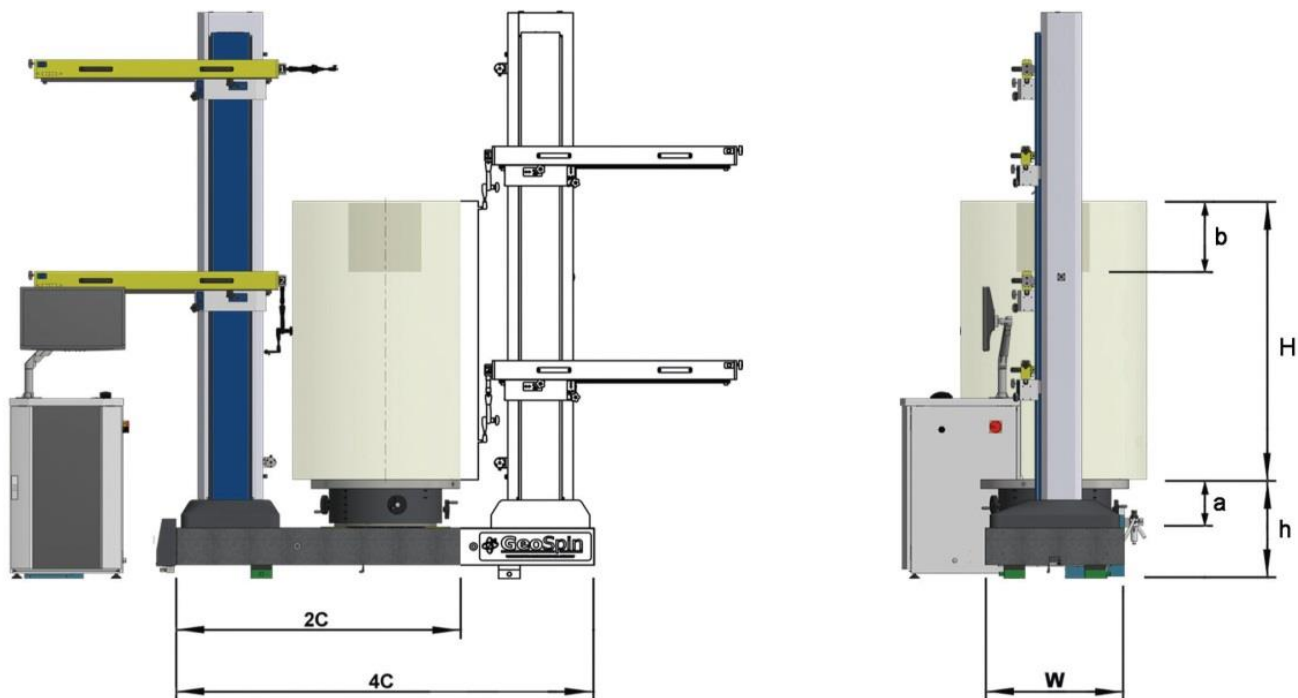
## PLATEFORMES DE MESURE ET D'ASSEMBLAGE DE ROTOR DE TURBINE INTÉGRÉES
